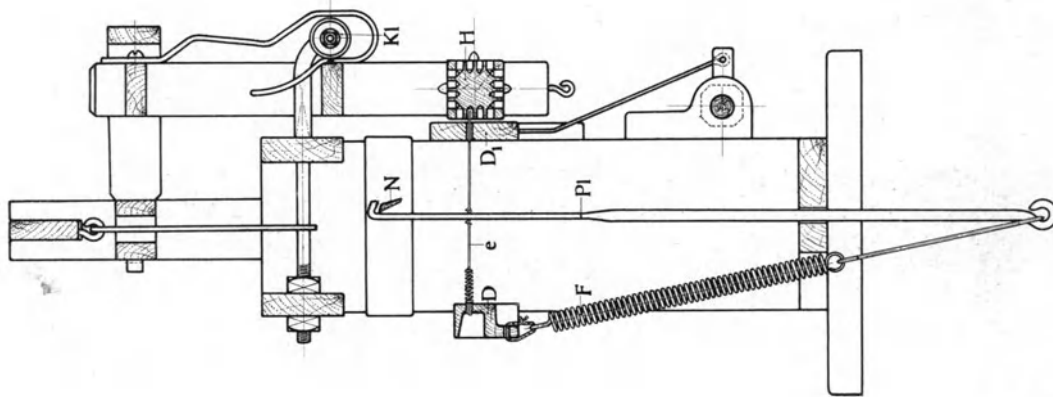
Die Handwebstuhl-schafftmaschine für damastartiges Gewebe mit einer Platinereihe.
